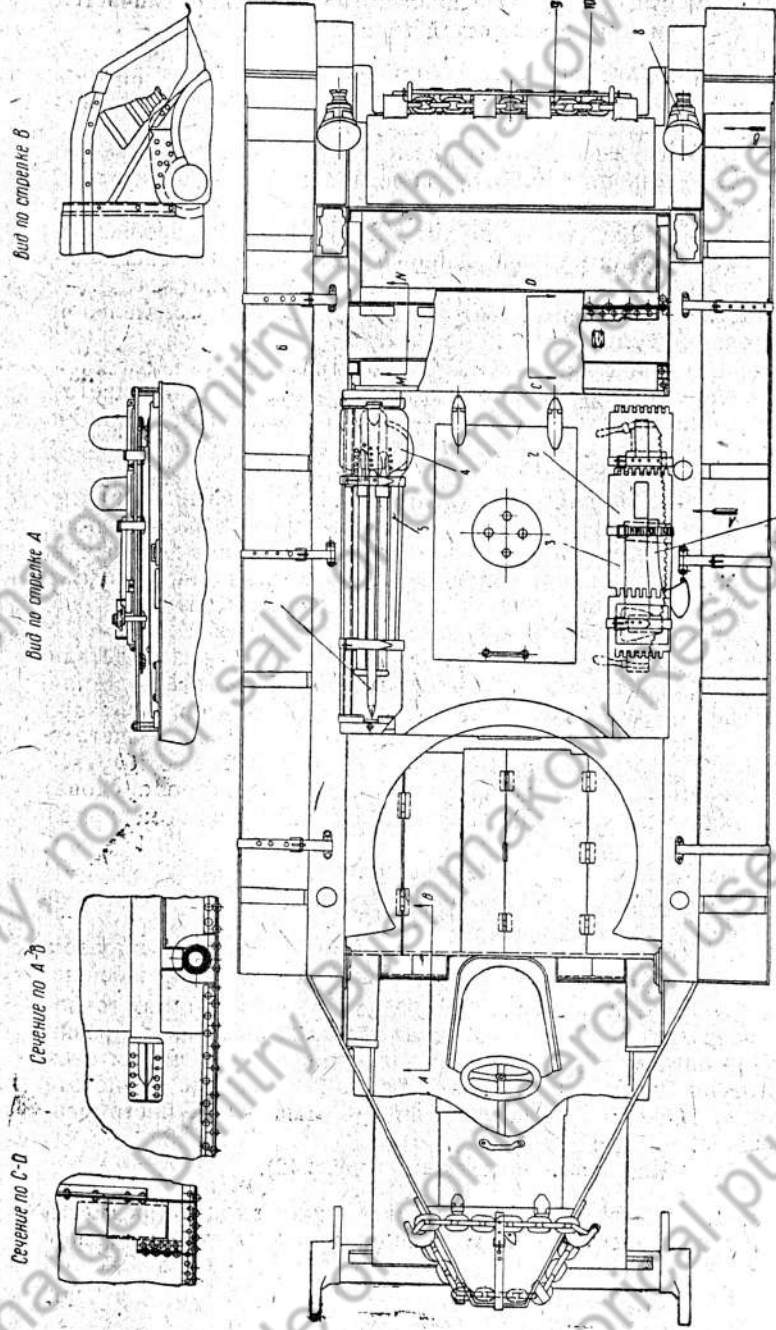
Общий вид укладки зап. частей шанцевого инструмента, подъемных и тяговых приспособлений снаружи танка.
